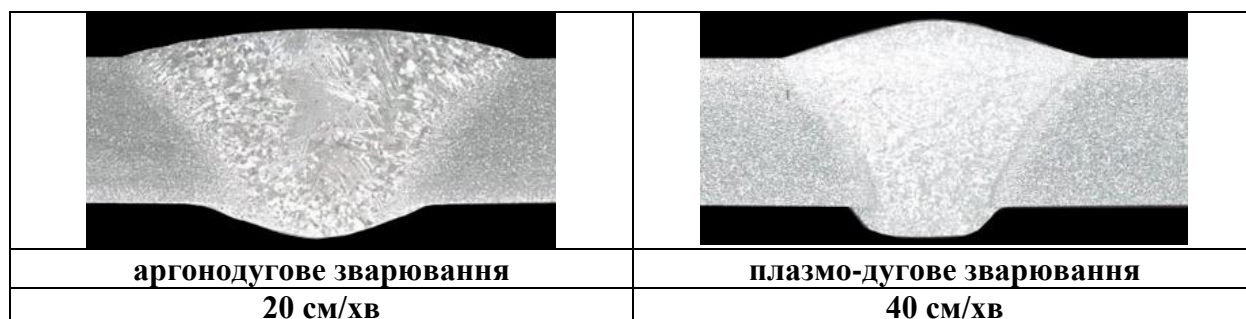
Поперечні шліфи зварного з'єднання листів товщиною 6,0 мм із сплаву АМг6Н отриманих різними способами зварювання неплавким електродом з використанням присадкового дроту СвАМг6.
